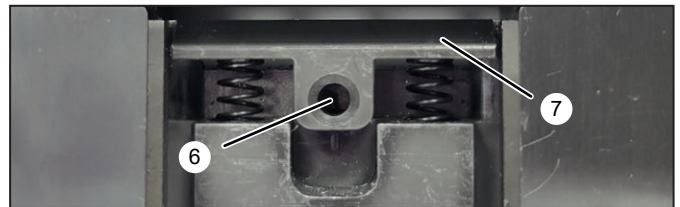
Gefederter Tisch, Steckplatz für Adapter
